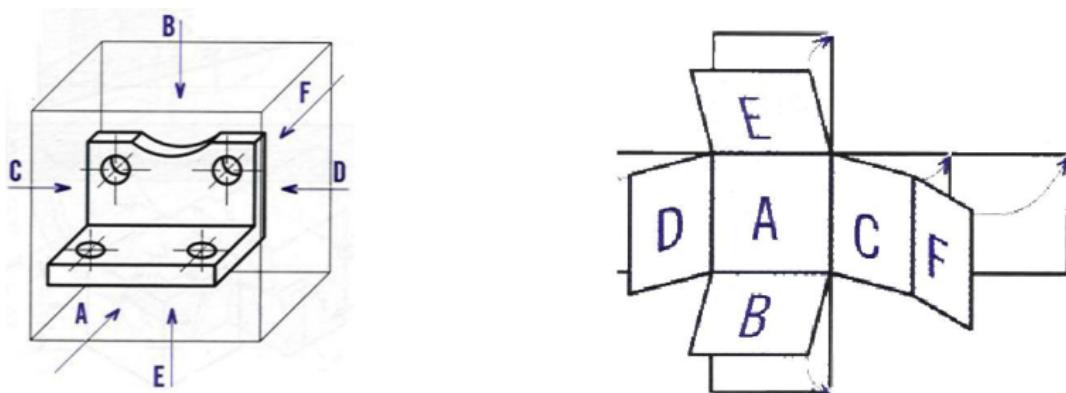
A : vue de Face - B : vue de dessus - C : vue de Gauche - D : vue de Droite - E : vue de dessous - F : vue de derrière (car on fait tourner la vue C)
